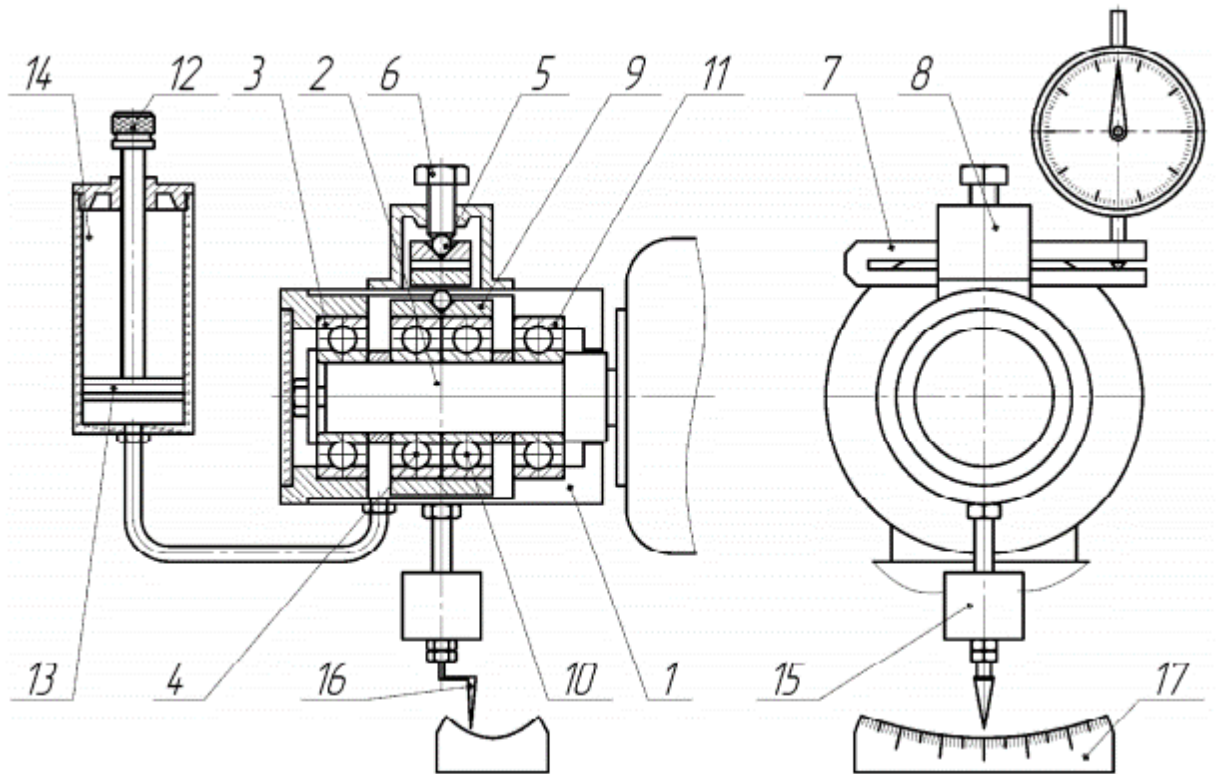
Схема лабораторної установки ДМ-28М: 1 – касета з підшипниками; 2 – вал; 3 – підшипник; 4 – тіло кочення; 5 – індентор; 6 – гвинт; 7 – динамометрична скоба; 8 – корпус; 9 – підшипник; 10 – тіло кочення; 11 – підшипник; 12 – клапан; 13 – поршень; 14 – циліндр; 15 – маятник; 16 – стрілка; 17 – шкала
